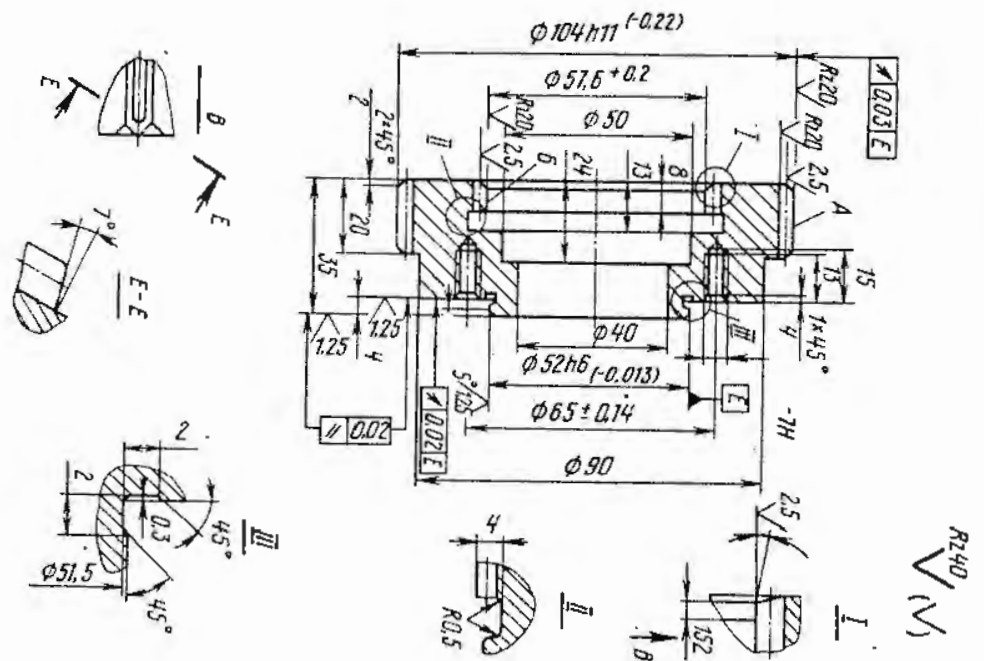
Колесо зубчатое, деталь № ЗЛ722А.322.401 НRC 22...30
